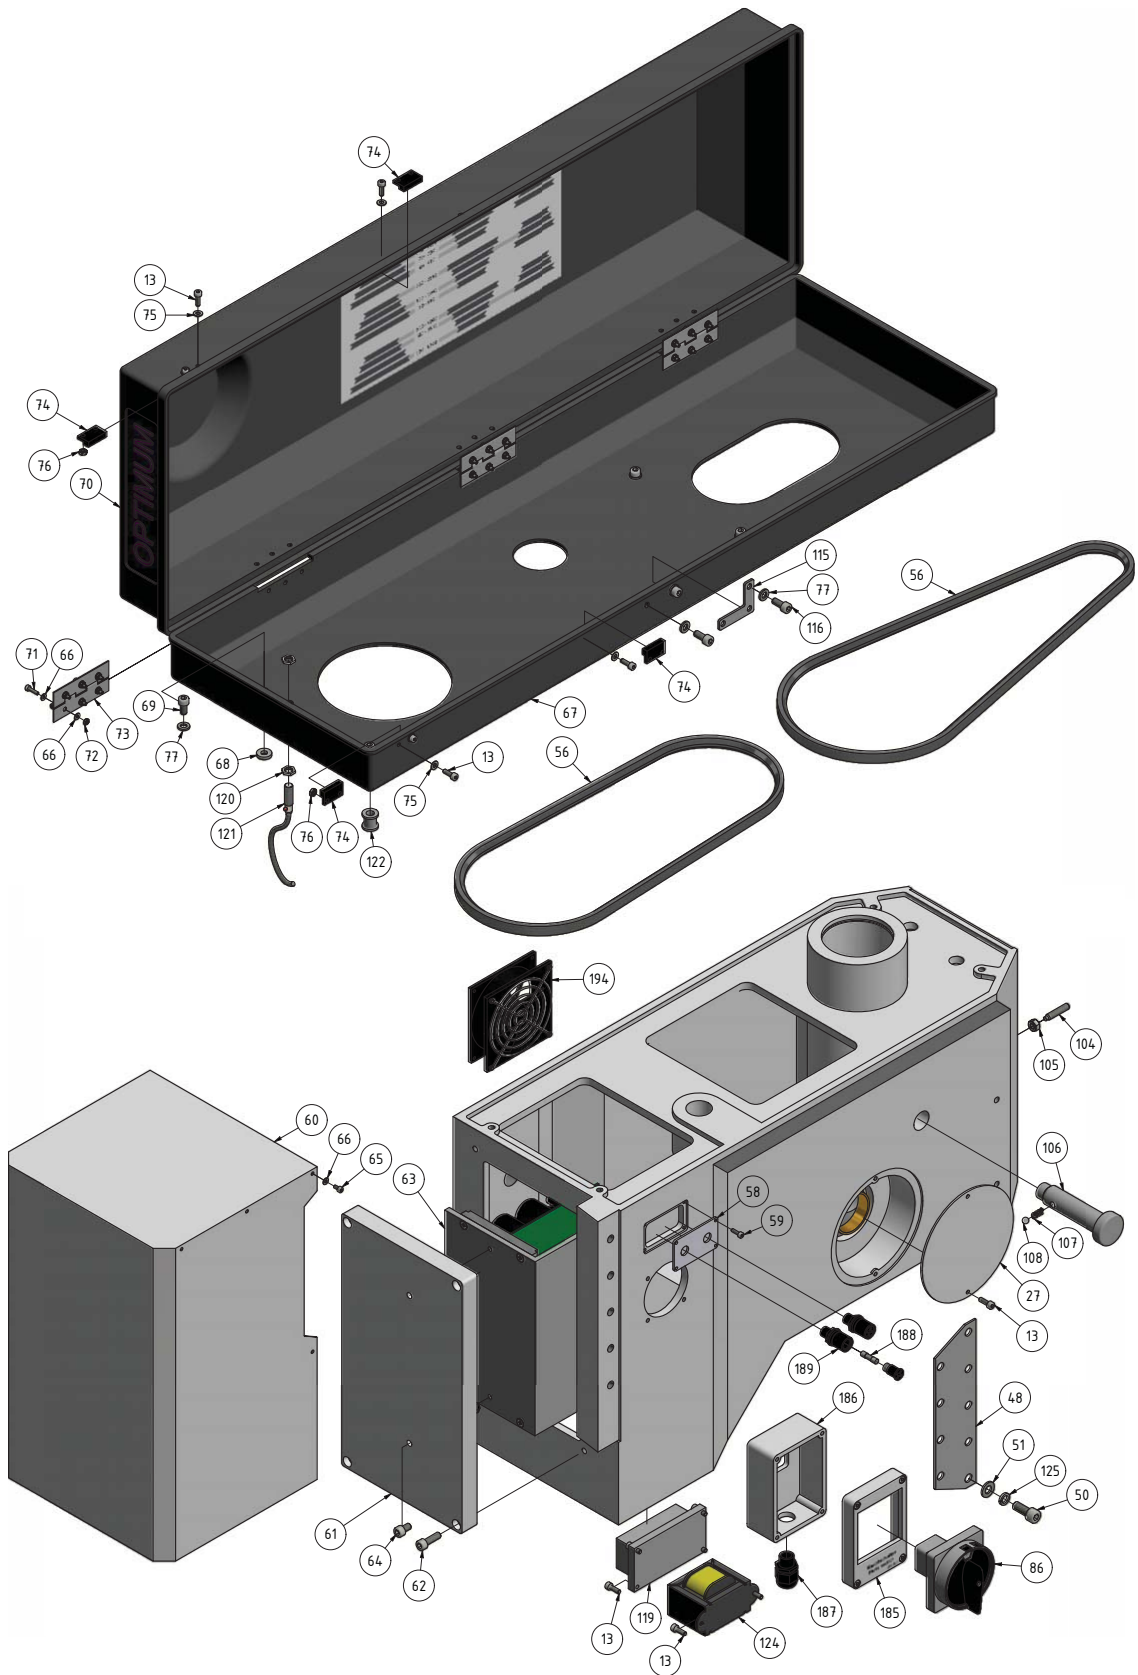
Bohrkopf 5 von 5 - Drilling head 5 of 5
